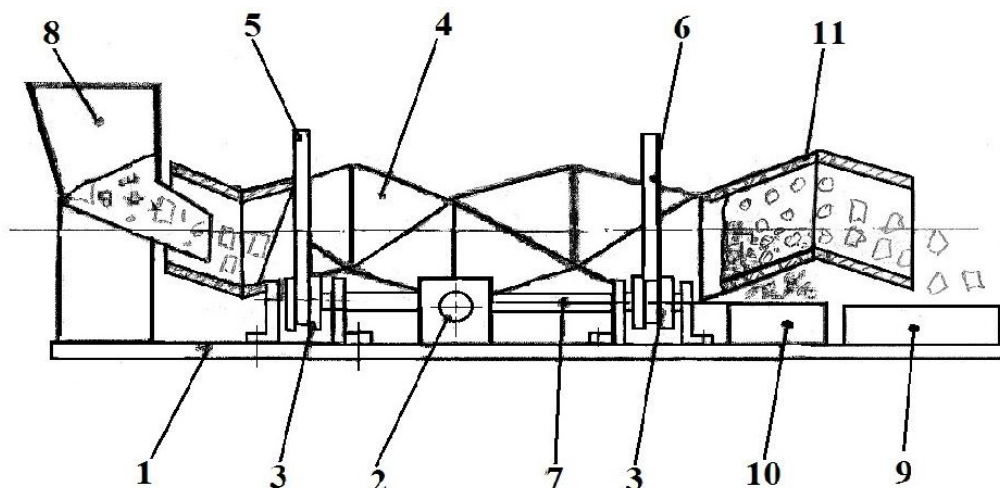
Схема станка на базе винтового ротора смонтированного из октаэдральных элементов, 1 - станина, 2 - привод главного движения, 3 - роликовые опоры, 4 - винтовой ротор, 5 и 6 - обода, 7 - два вала на которых закреплены роликовые опоры 3, 8 - средство для загрузки, 9 - бункер для приема обработанных деталей, 10 - бункер для приема рабочих сред, 11-отверстия для удаления рабочих сред.
